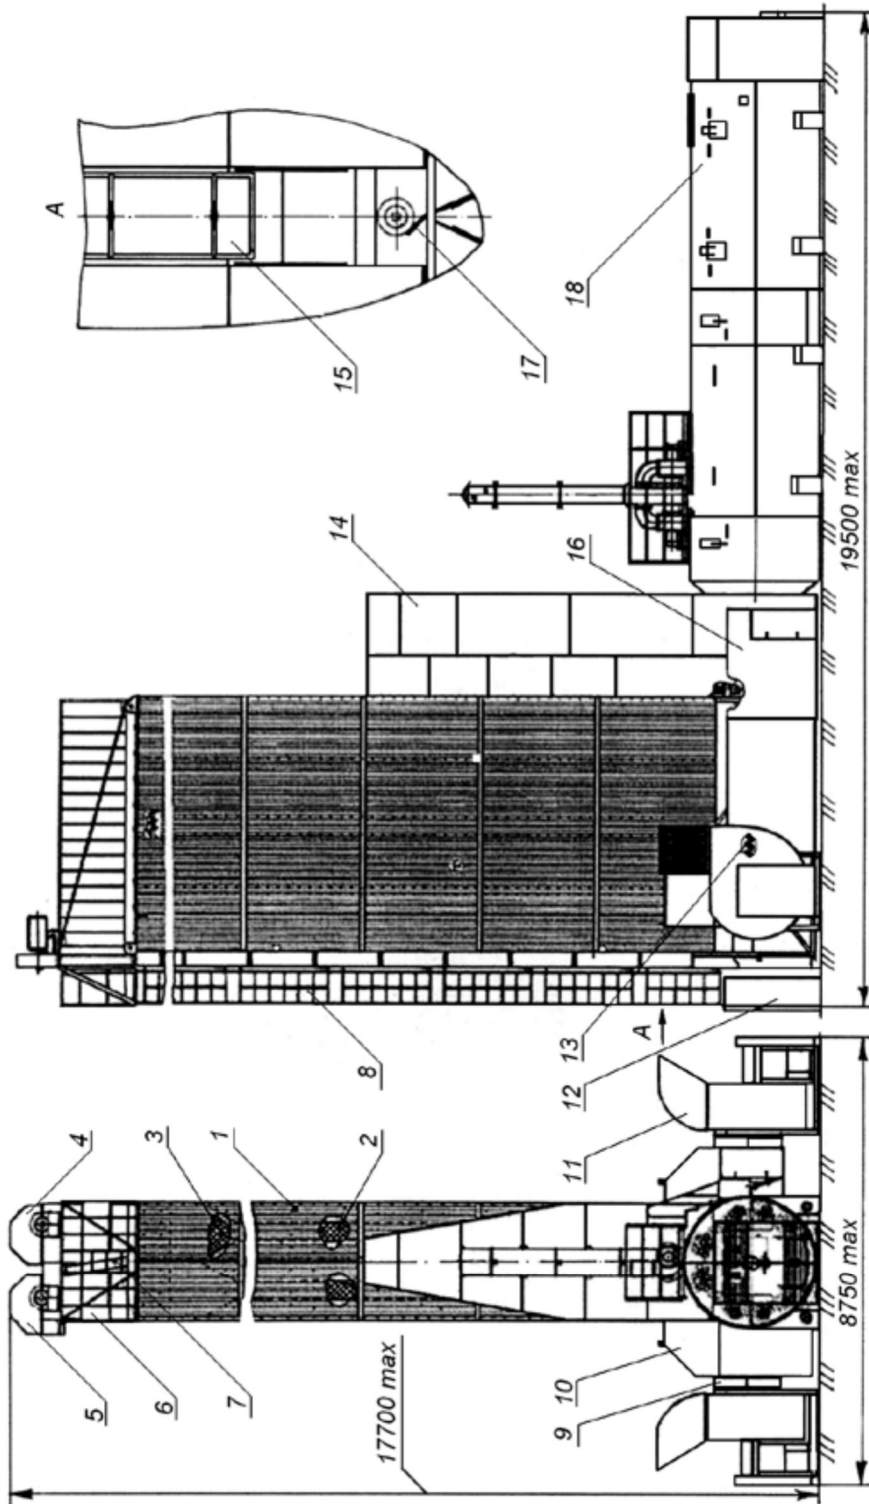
Зерносушилка СЗК-20: 1 – корпус; 2 – сушильная колонка; 3 – приемный бункер; 4 – нория загрузки; 5 – нория выгрузки; 6 – площадка обслуживания; 7 – зернопровод; 8 – лестница; 9 – соединительный рукав; 10, 14, 16 – воздуховоды; 11 – вентилятор; 12 – электрошкаф управления; 13 – шнек; 15 – дверь задняя; 17 – распределитель зерна; 18 – воздухонагреватель ВУ-Т-1,5
